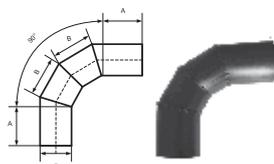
Отвод 90° сварной 4-х сегментный
